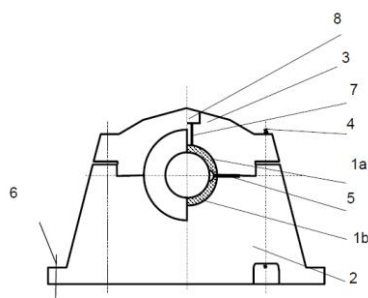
Lagăr cu alunecare. Elemente componente: cuzinet – 1a, 1b; corp – 2; capac – 3; elemente de asamblare – 4; elemente de reglaj- 5; șurub de fixare în fundație – 6; canal de ungere – 7; dispozitiv de ungere – 8. [3]
